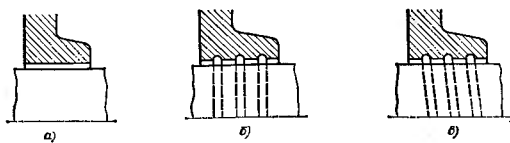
Уплотнения щелевого типа: а — с кольцевым зазором; б — с кольцевыми канавками; в — с кольцевыми канавками винтового типа
